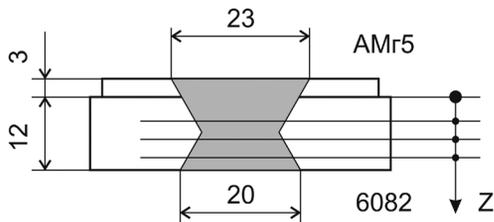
Условная схема поперечного сечения образца сварного шва при сварке внахлест пластин из сплавов АМг5 и 6082
